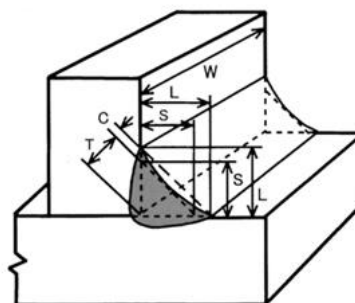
Dimensiones de soldadura de filete[63]
